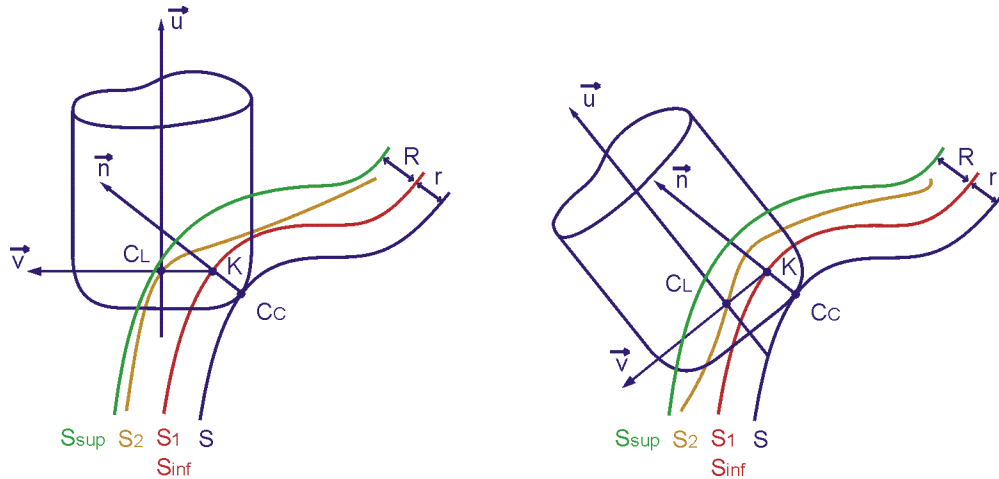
Surface d'usinage en 5 axes avec outil torique [TOURNIER et al. 02]
